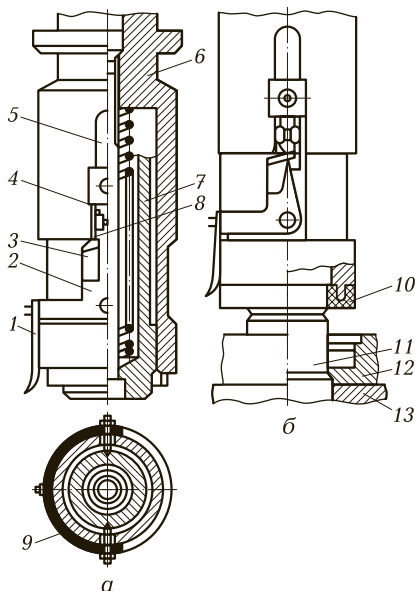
Инструмент для запрессовки резиновой уплотнительной манжеты:
